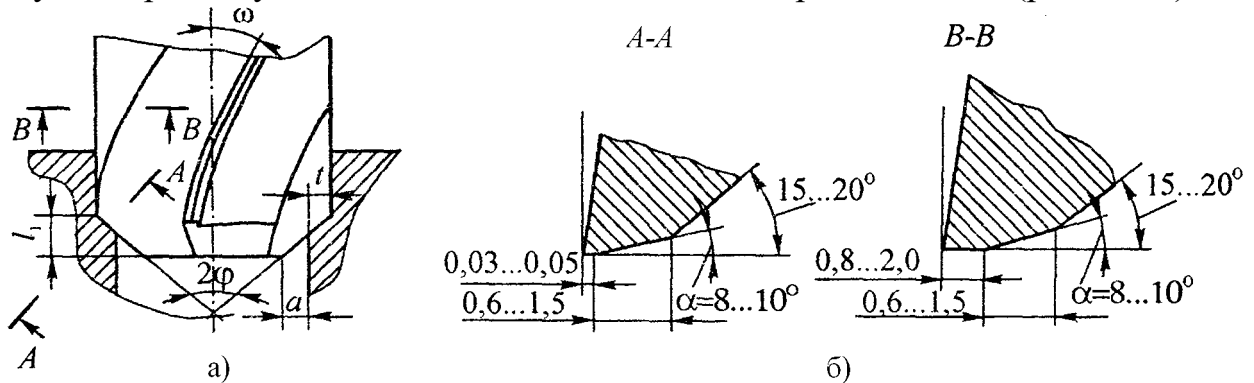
Режущая часть цилиндрического зенкера: а – элементы режущей части; б – формы заточки зубьев зенкера
